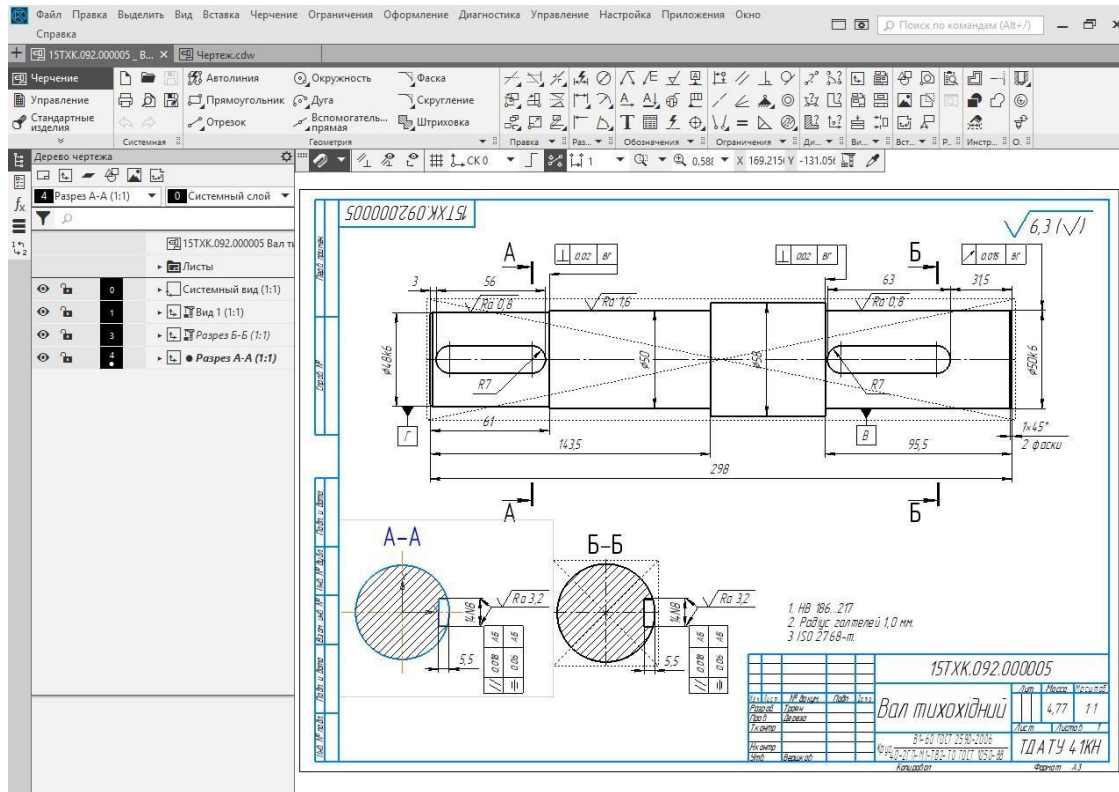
Робочий кресленик вала в КОМПАС 18
